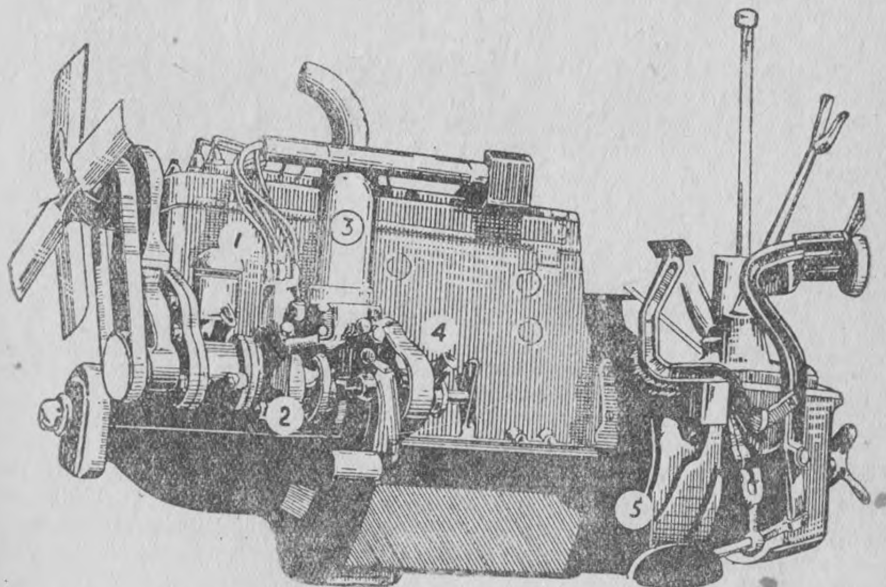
Двигатель «АМО» (вид с левой стороны).
